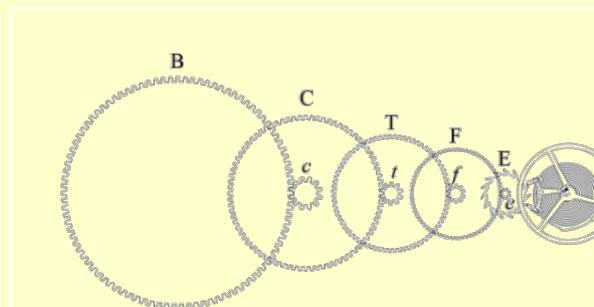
Tren de engranajes típico de un reloj mecánico.
